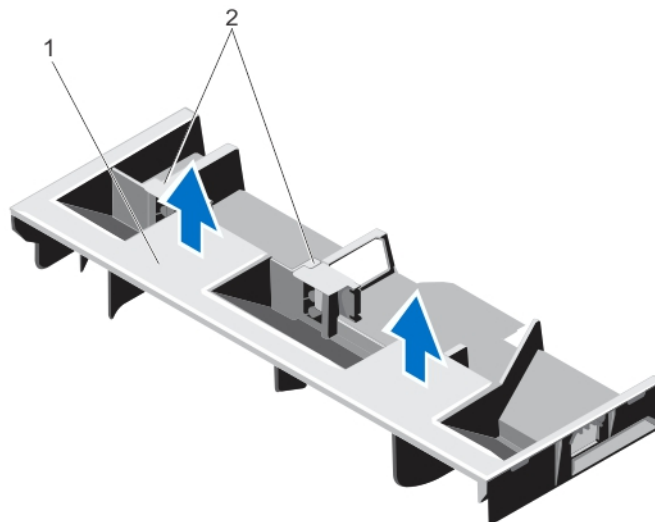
Extracción e instalación de la cubierta de refrigeración
